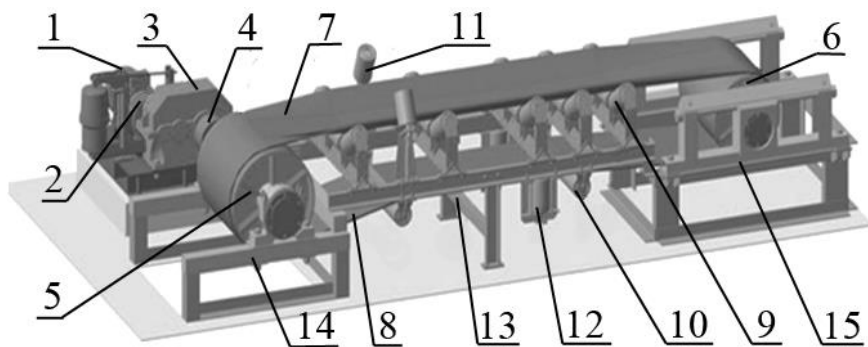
Конструкція та основні вузли стрічкового конвеєра
